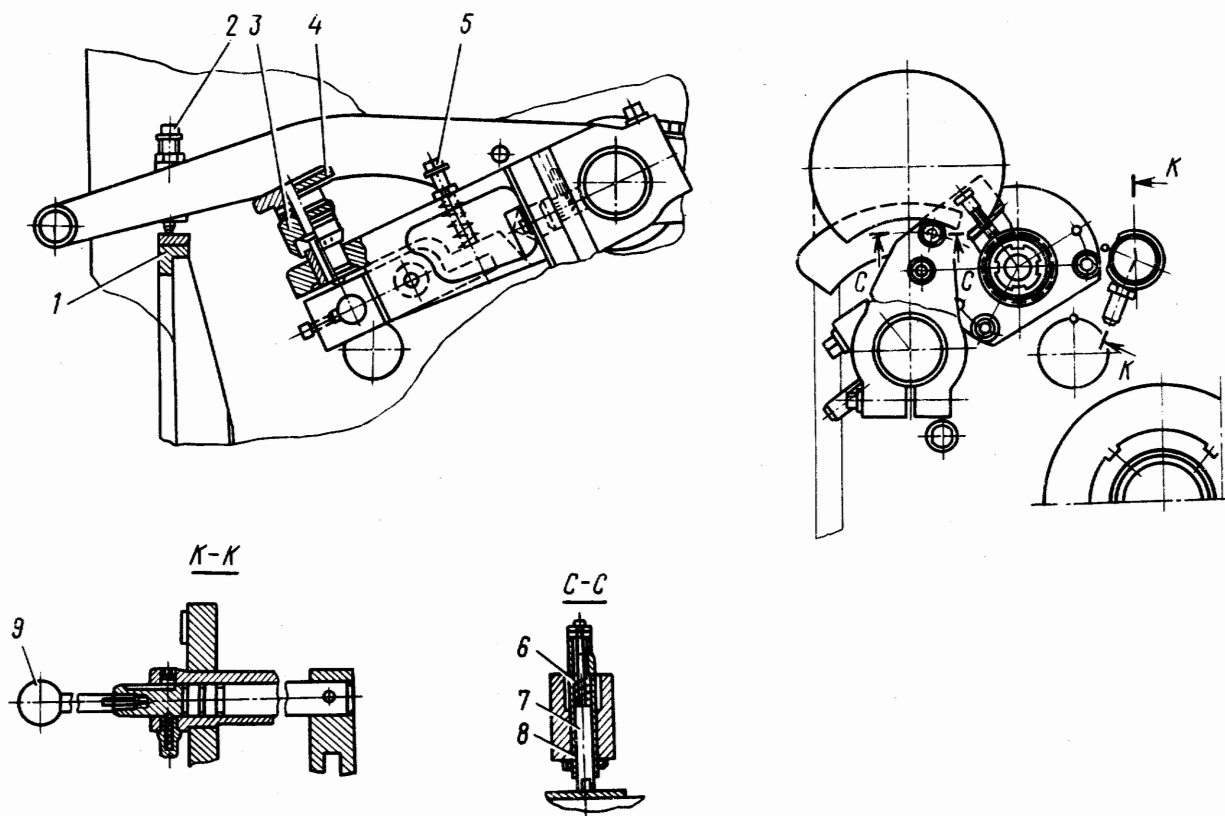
Резьбонарезное устройство. Отдельные виды и разрезы
